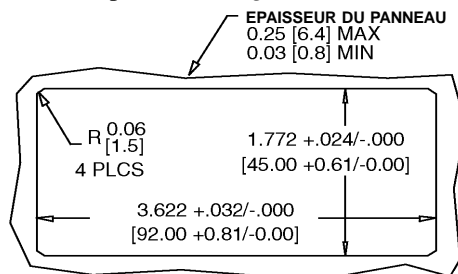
Dimensions du perçage pour montage panneau en pouces (en millimètres entre parenthèses)
